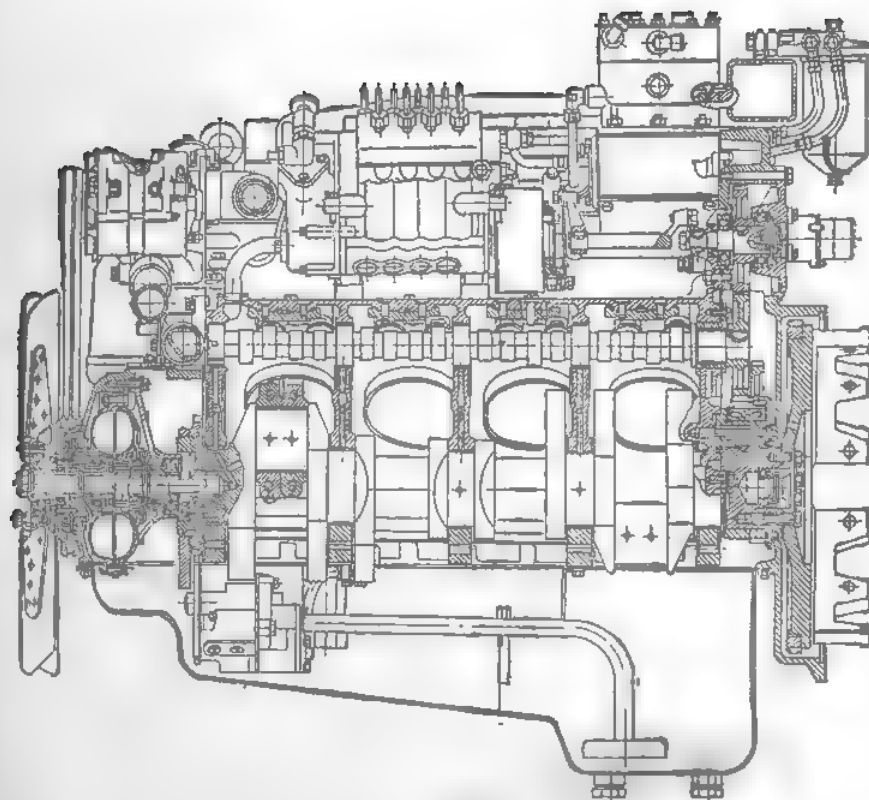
Продольный разрез двигателя ЯМЗ-740
